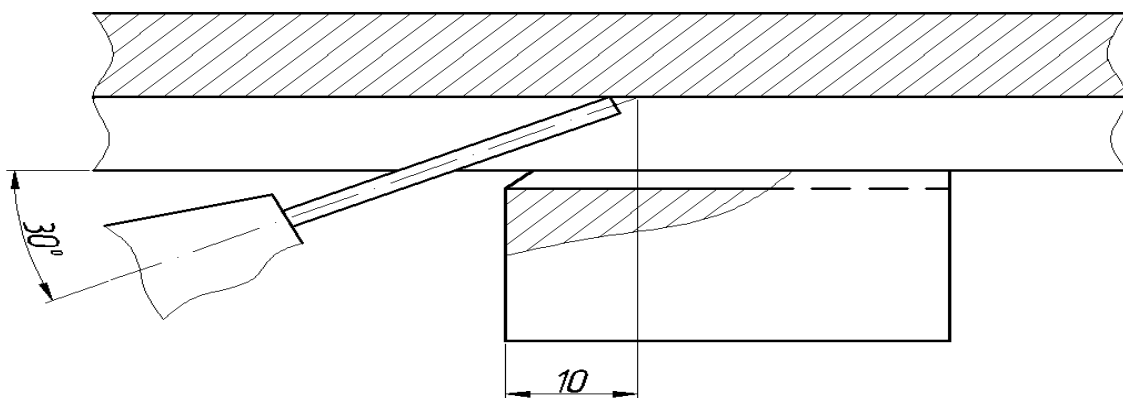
Схема розміщення порошкового дроту на старті зварювання
